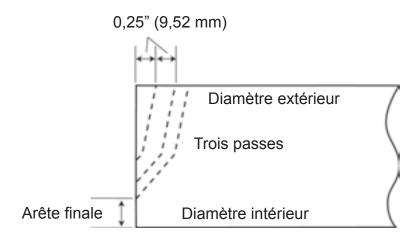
Le dessin illustre l'usinage d'un chanfrein composé en plusieurs passes. Réglez la profondeur du porte-outil à environ 1/4" (6,35 mm) en arrière le long du diamètre extérieur du tuyau pour chaque passe.
